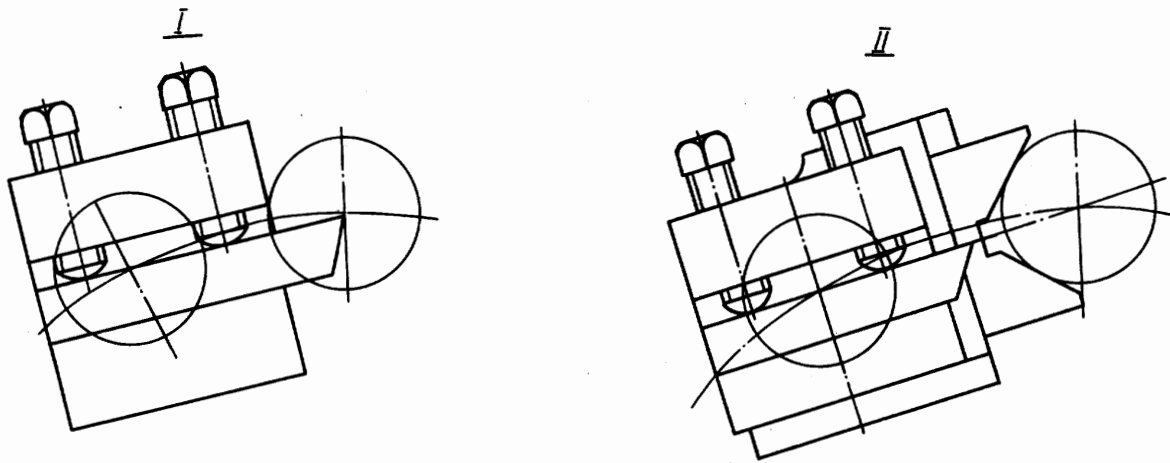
Схема наладки инструмента вне станка. Установка „по центру“:
